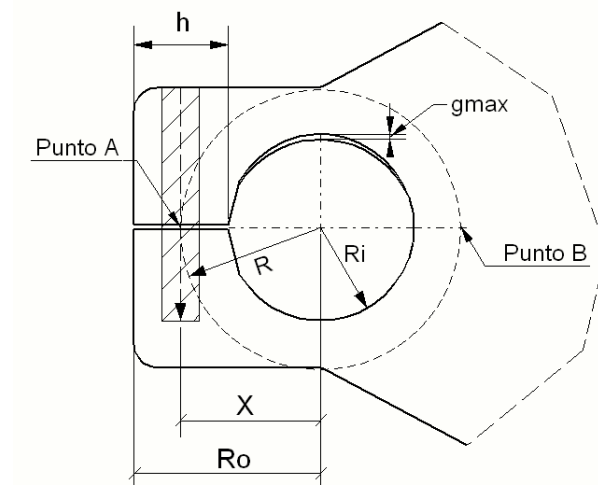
vista de planta sistema travesaño – columna (sujetador)
